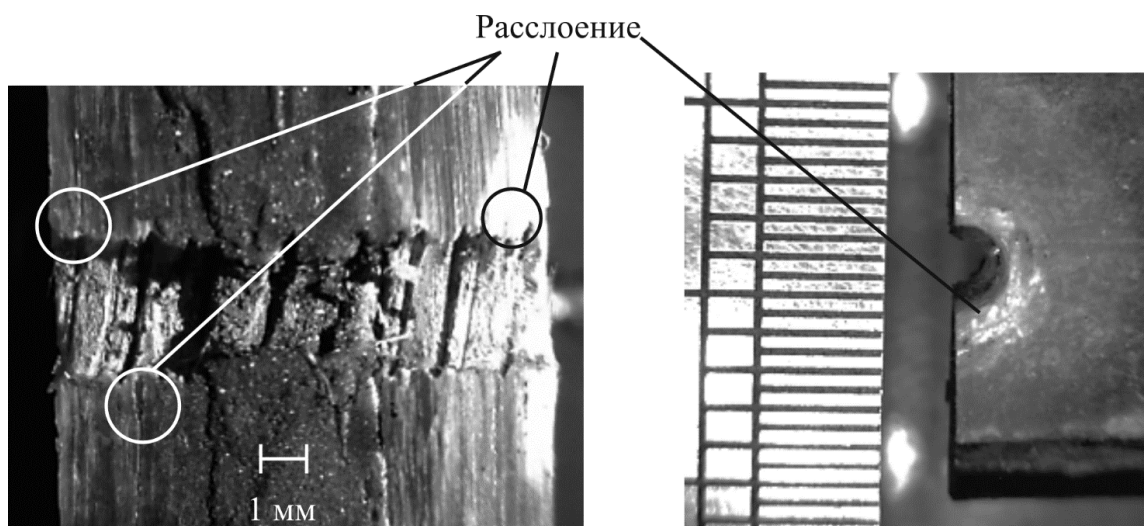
Повреждения в стеклопластике в результате сверления отверстия и монтажа армирующего элемента: а) поперечный разрез б) вид сверху
